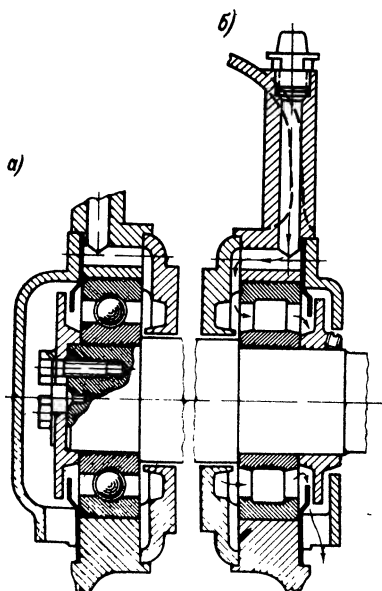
Узлы шарикоподшипников малых машин фирмы «ASEA»: а — передний подшипник; б — подшипник со стороны привода
